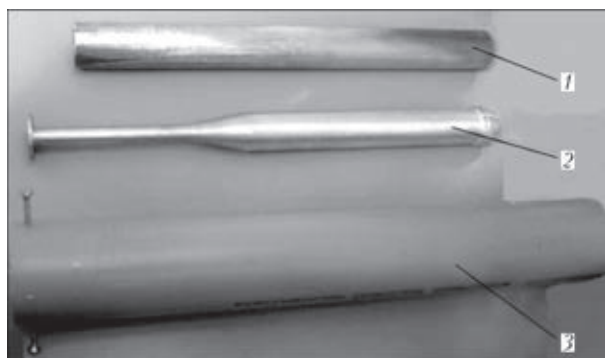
Основные составляющие элементы для сварки взрывом биметаллического прутка: 1 — медная трубка; 2 — алюминиевый пруток; 3 — полиэтиленовая труба, служащая контейнером для взрывчатого вещества
